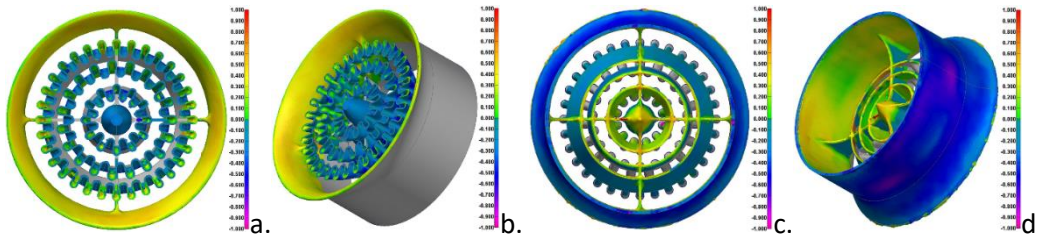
Măsurători pentru tehnica SLA - a. Vedere frontală; b. Vedere din partea de jos, în stânga c. Vedere din spate; d. Vedere din partea de jos, în dreapta
